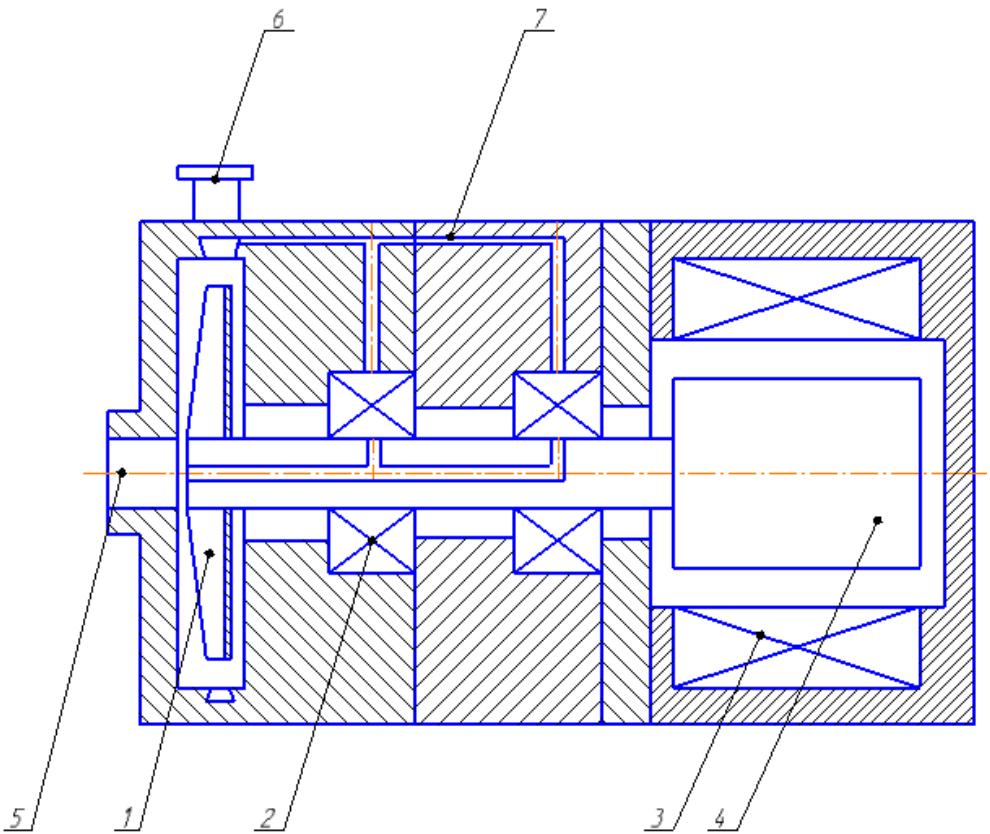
Устройство и основные детали малорасходного центробежного консольного насоса с гидростатическими подшипниками:
